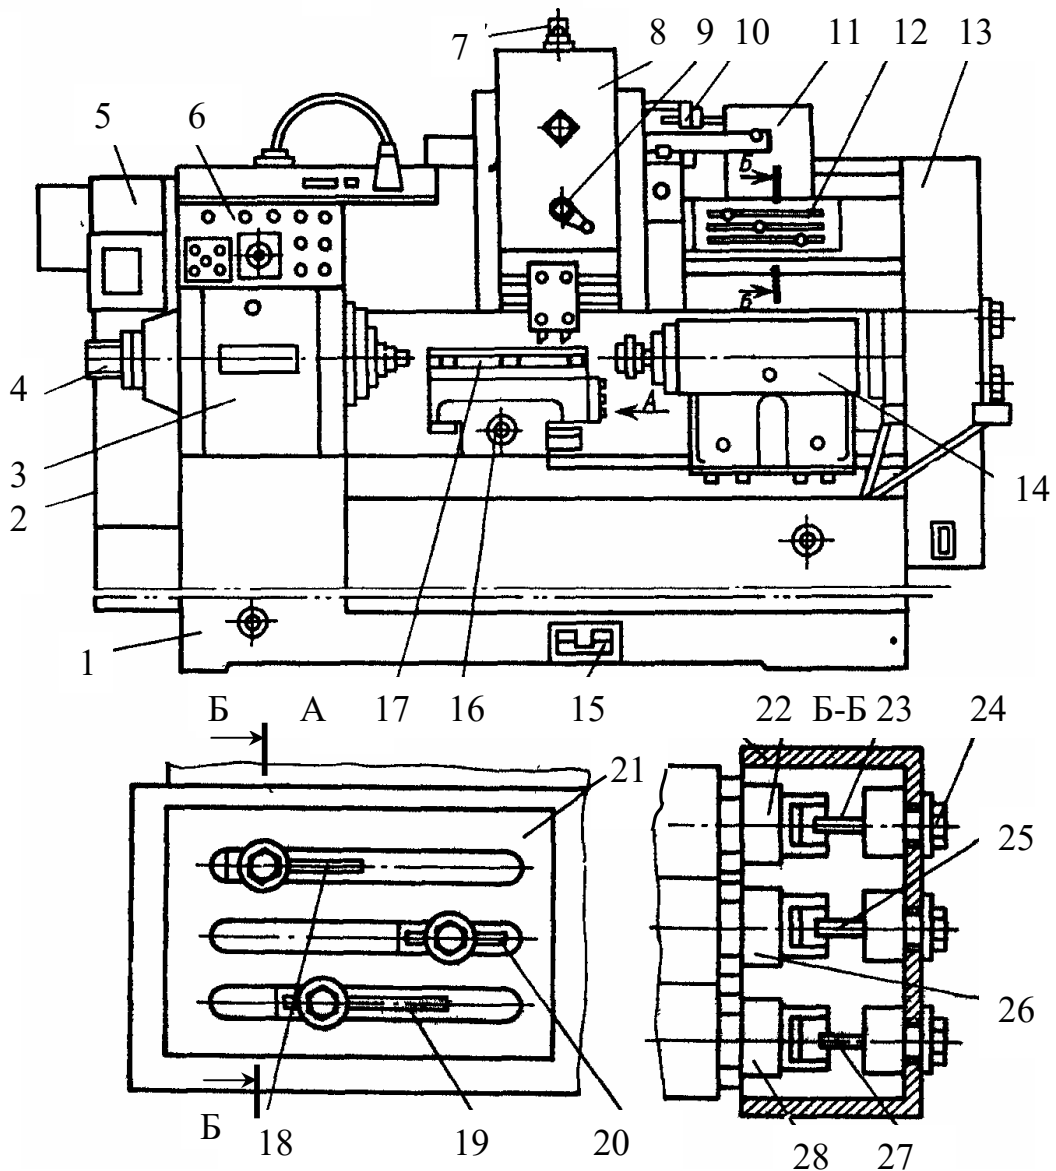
Багаторіздевий токарний напівавтомат: 1 – станина; 2 – привод шпинделя; 3, 14 – передня і задня бабки; 4 – шпиндель; 5 – коробка подач повздовжнього супорта; 6 – пульт керування; 7, 9, 16 – гвинти ручного переміщення супортів; 8, 17 – повздовжній і поперечний супорти; 10 – копіювальна лінійка; 11 – траверса; 12, 21 – пристрої керування повздовжнього та поперечного супортів; 13 – електрошафа; 15 – педаль переміщення задньої бабки; 18, 19, 20, 23, 25, 27 – кулачки керуючого пристрою; 22, 26, 28 – мікроперемикачі; 24 – гайки фіксації кулачків
